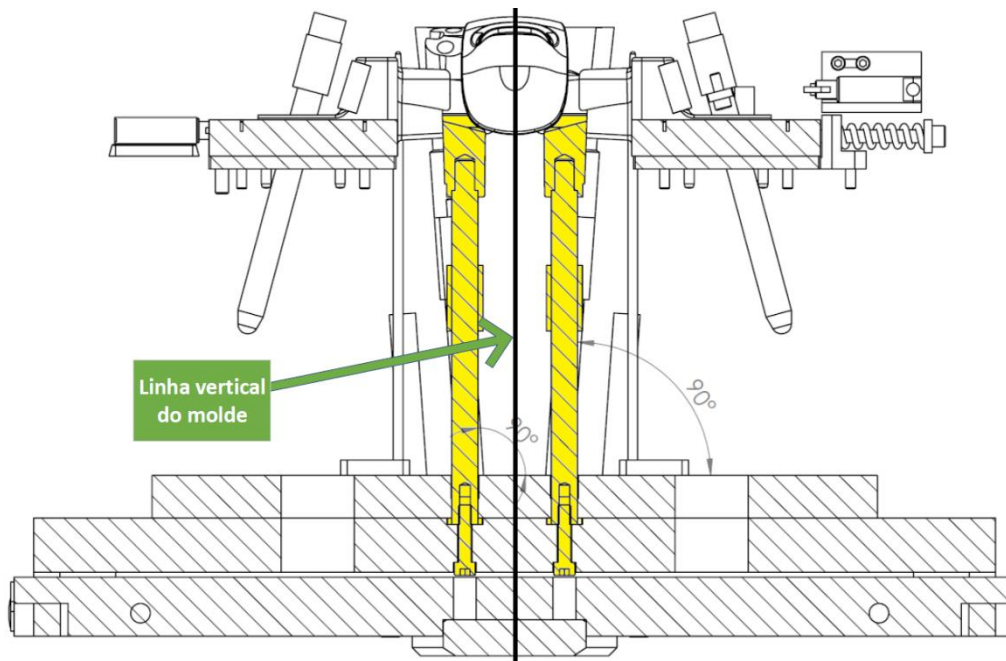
Desenho técnico da vista em corte dos levantadores a 90°
